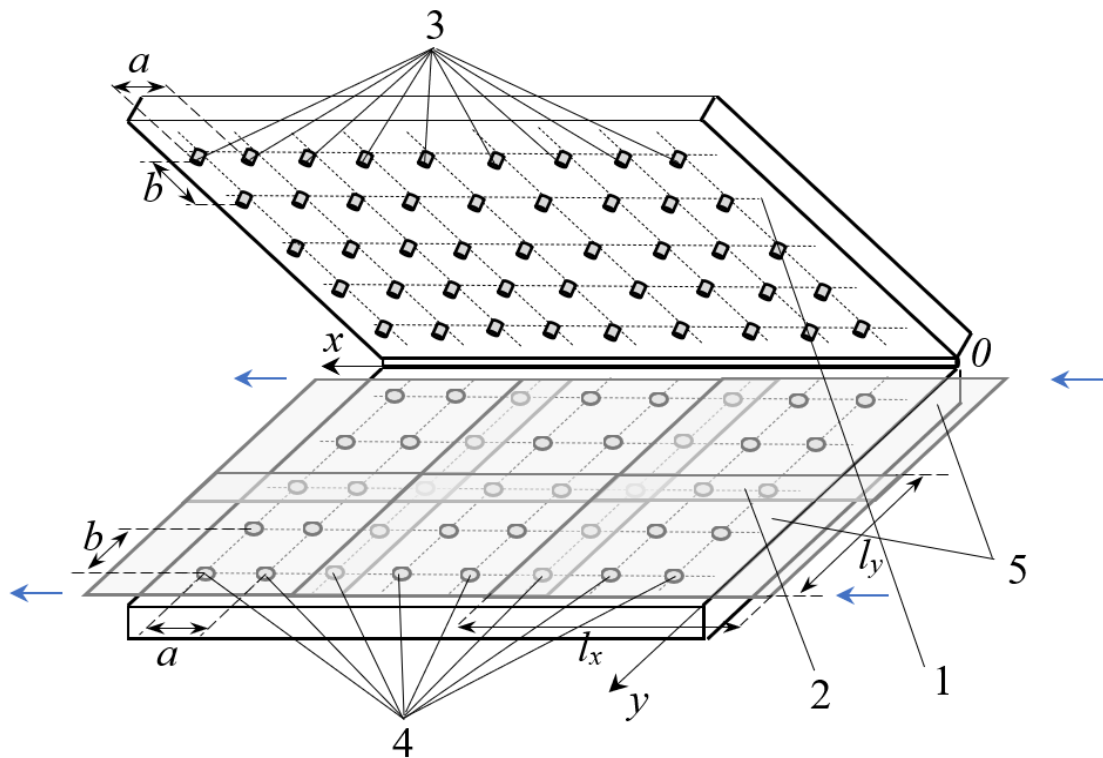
Загальний вигляд робочих поверхонь для зшивання кишкової сировини:
